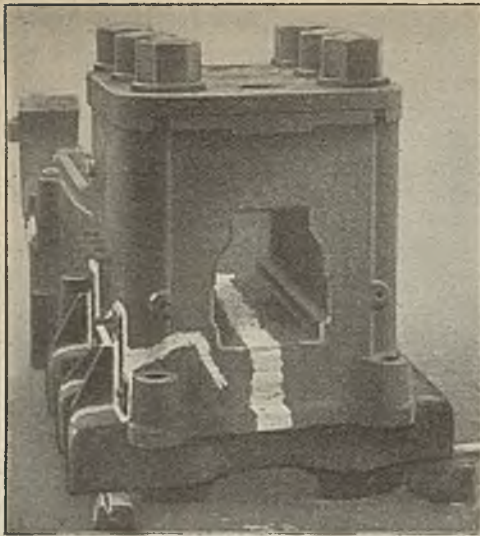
Geschweißter Brikettpressenkopf.
